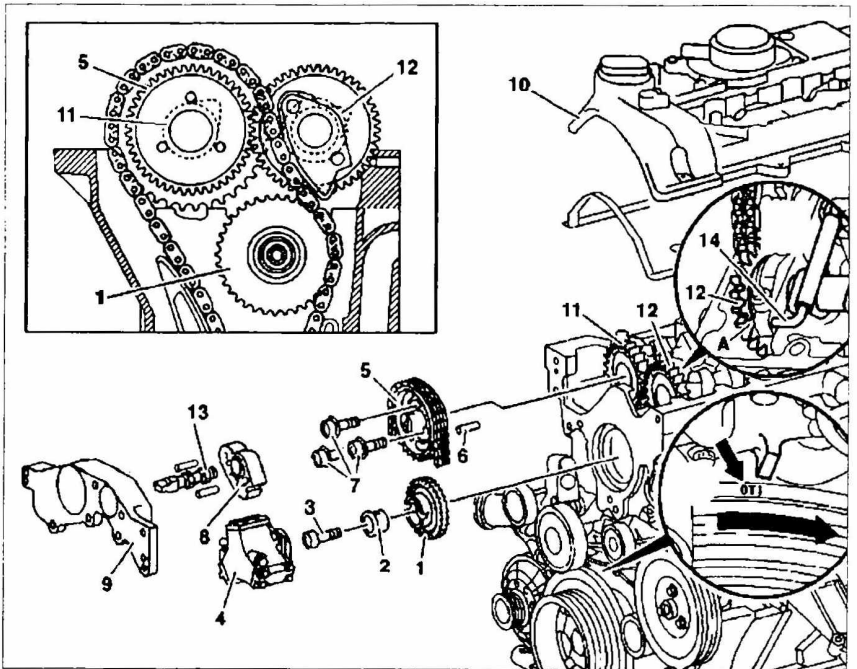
Снятие и установка промежуточной шестерни привода ТНВД:
